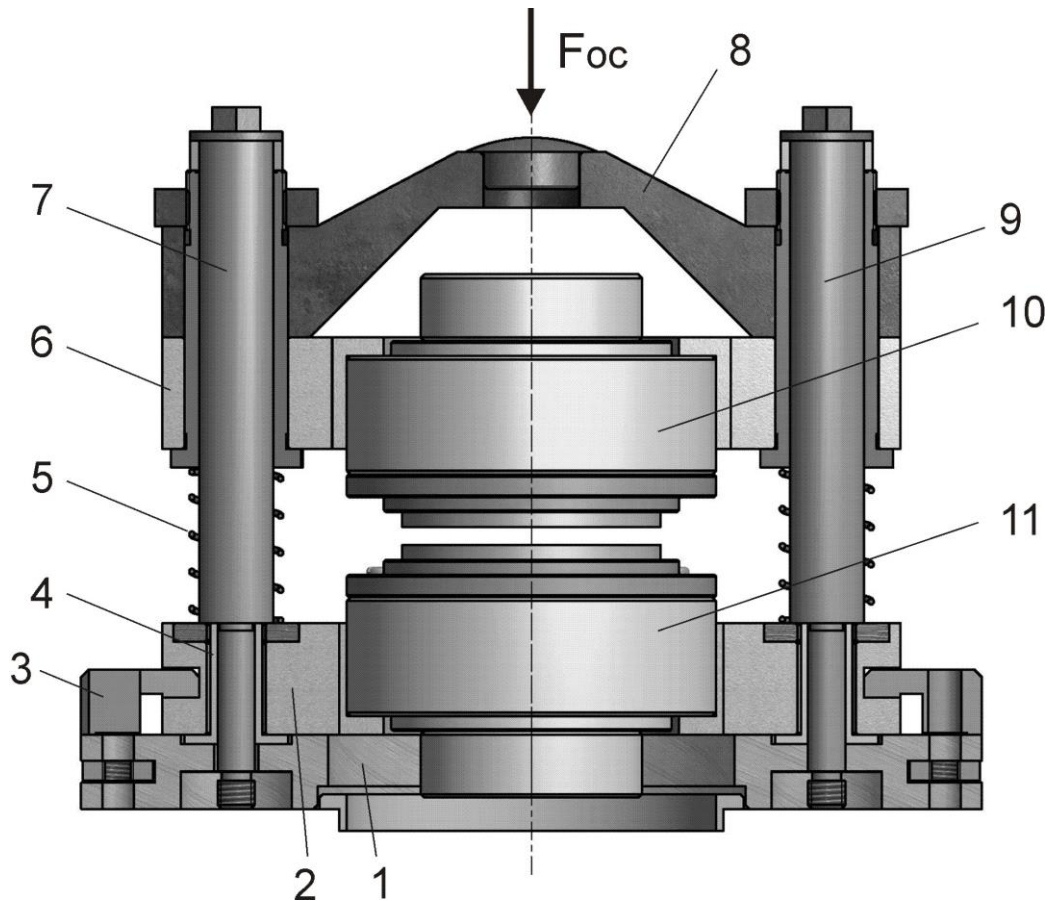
Установочное приспособление для сварки трубных заготовок переходников диаметром 70 мм
